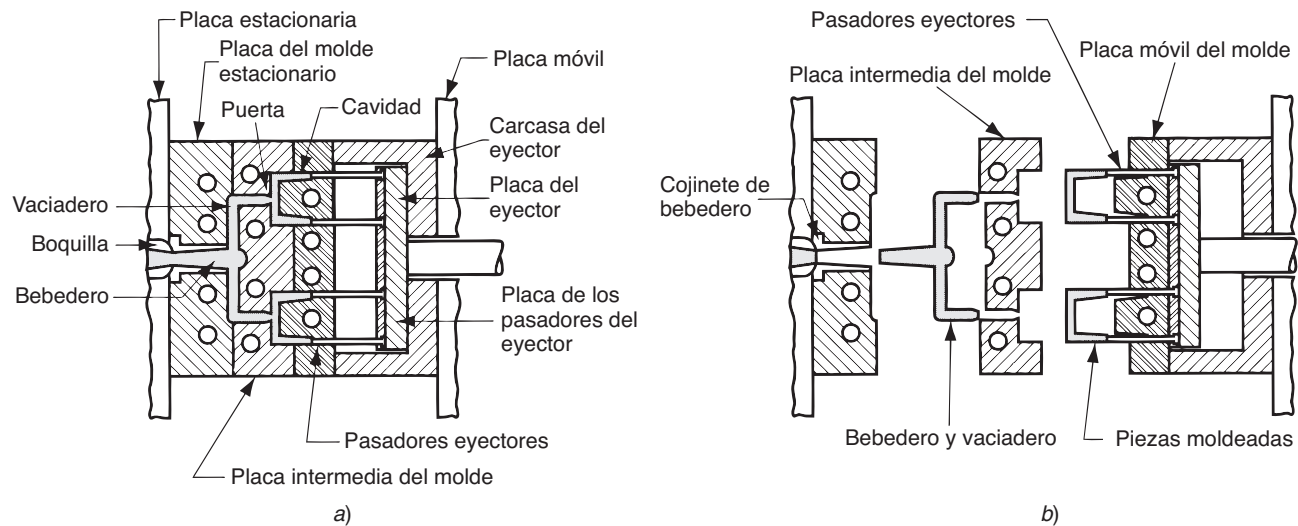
Molde de tres placas: a) cerrado y b) abierto.
